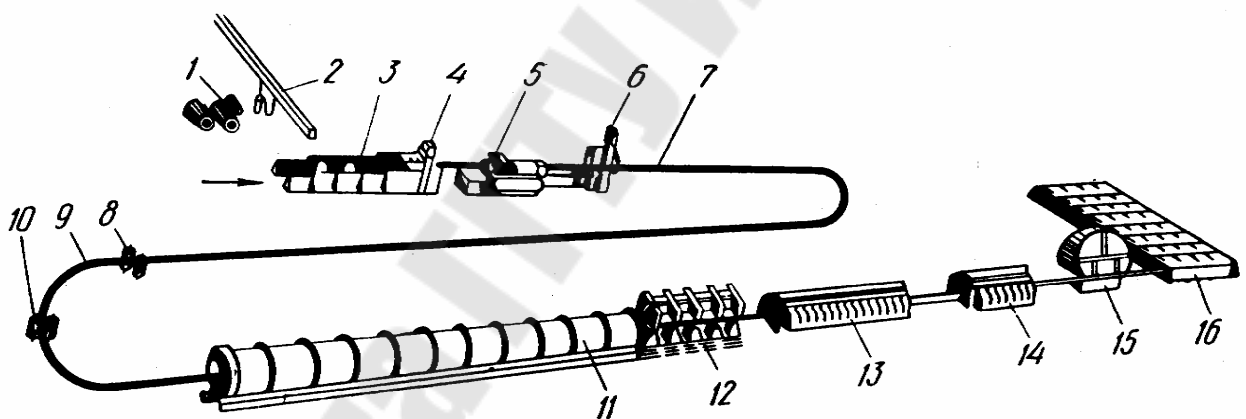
Схема технологического процесса производства труб непрерывной печной сваркой
